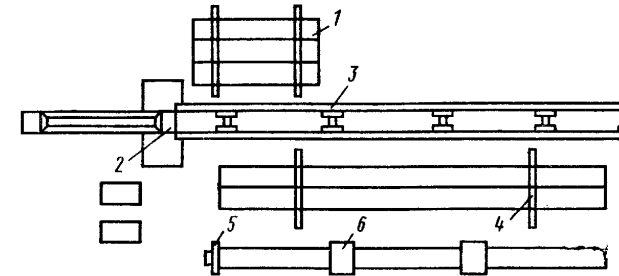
Схема механизированной линии для сварки поворотных стыков труб
